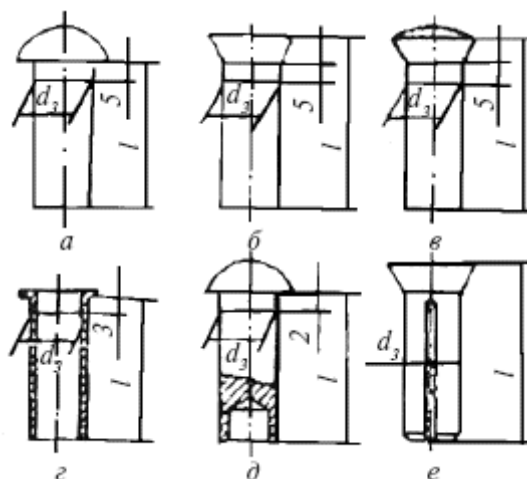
Заклепки: а – с полукруглой головкой; б – с потайной головкой; в – с полупотайной головкой; г – трубчатая; д – взрывная; е – разрезная
